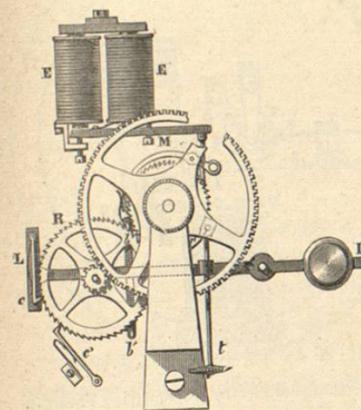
Indicador del contador electro-cronométrico Garnier
